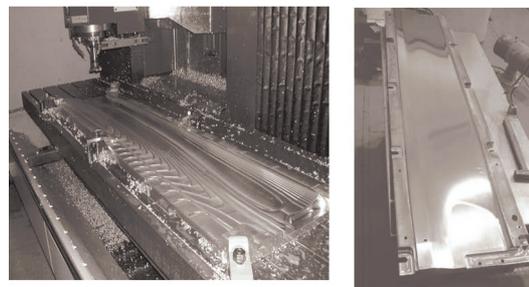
Изготовление формообразующей матрицы лопасти РВ.
